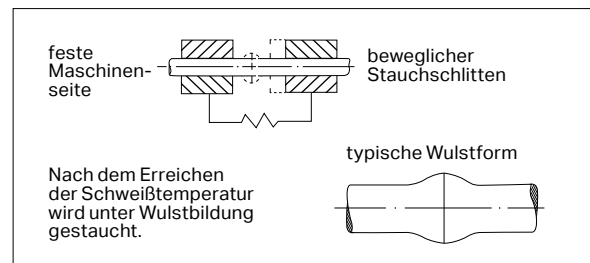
Prinzip des Press-Stumpfschweißens ⁽¹³⁾
